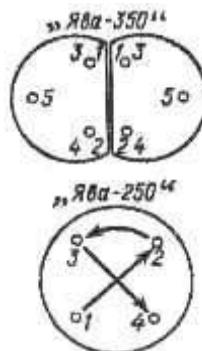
Схема порядка затяжки гаек на шпильках цилиндров
